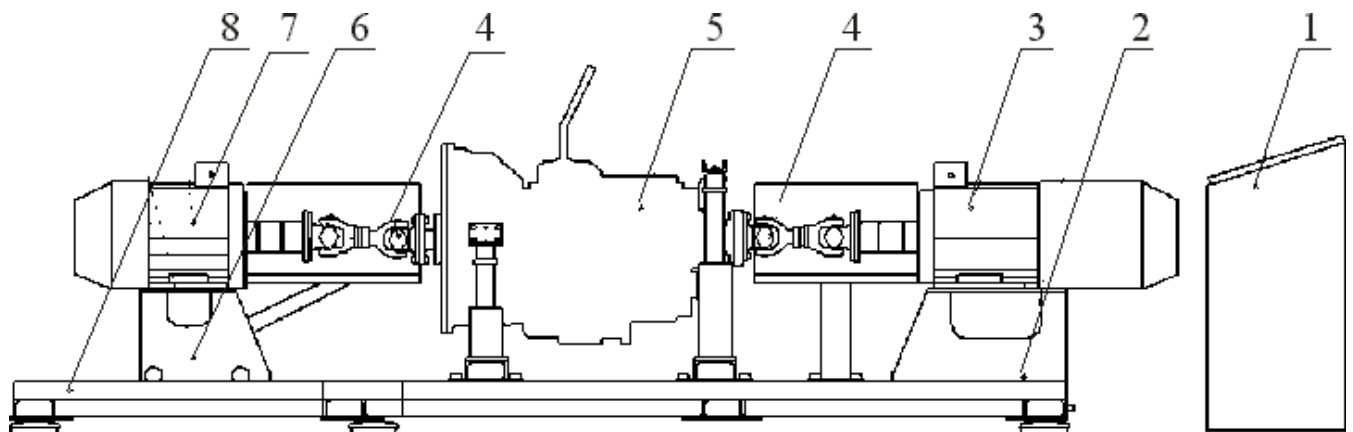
Стенд для обкатки та випробування коробок передач КС-02
